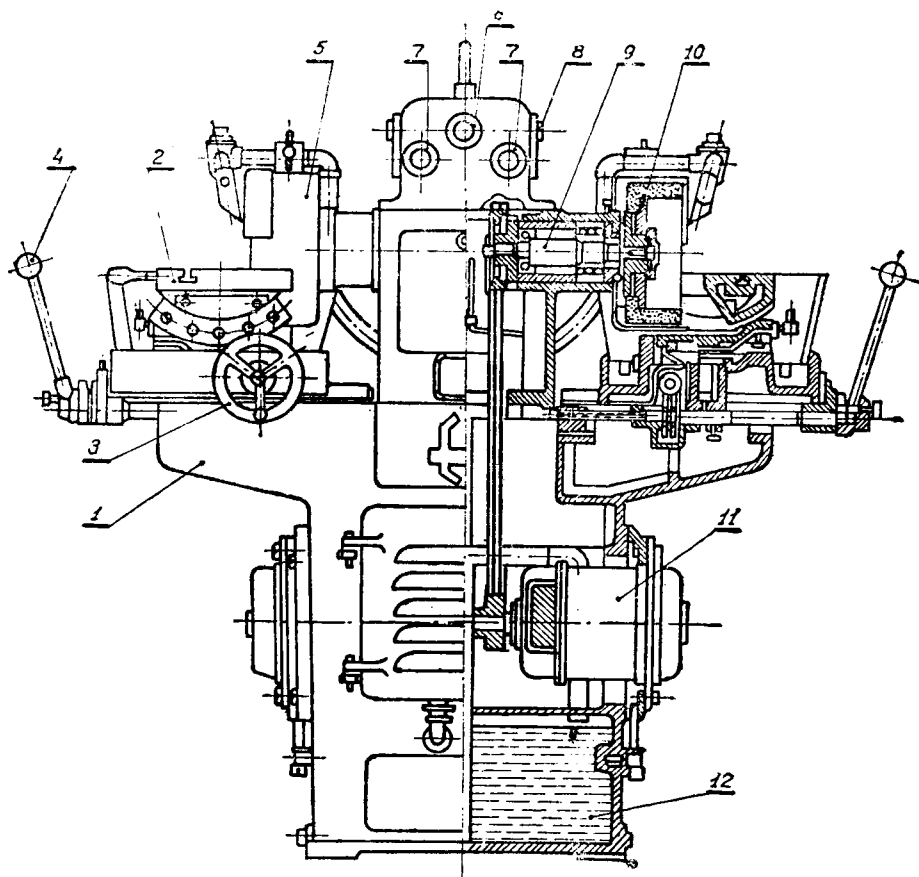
Станок для заточки резцов типа 362В завода им Кирова
